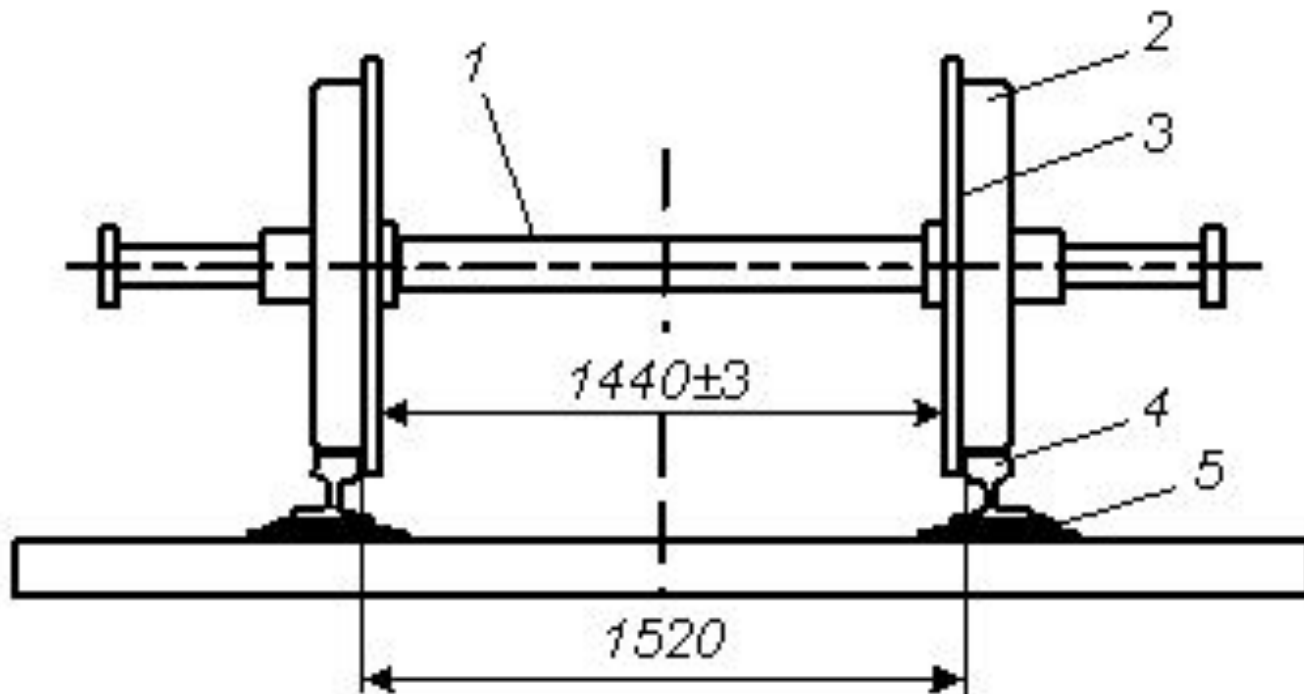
Колесная пара на рельсовой колее: 1 – стальная ось; 2 – колесо; 3 – направляющий гребень; 4 – рельс; 5 – подкладка под рельс
